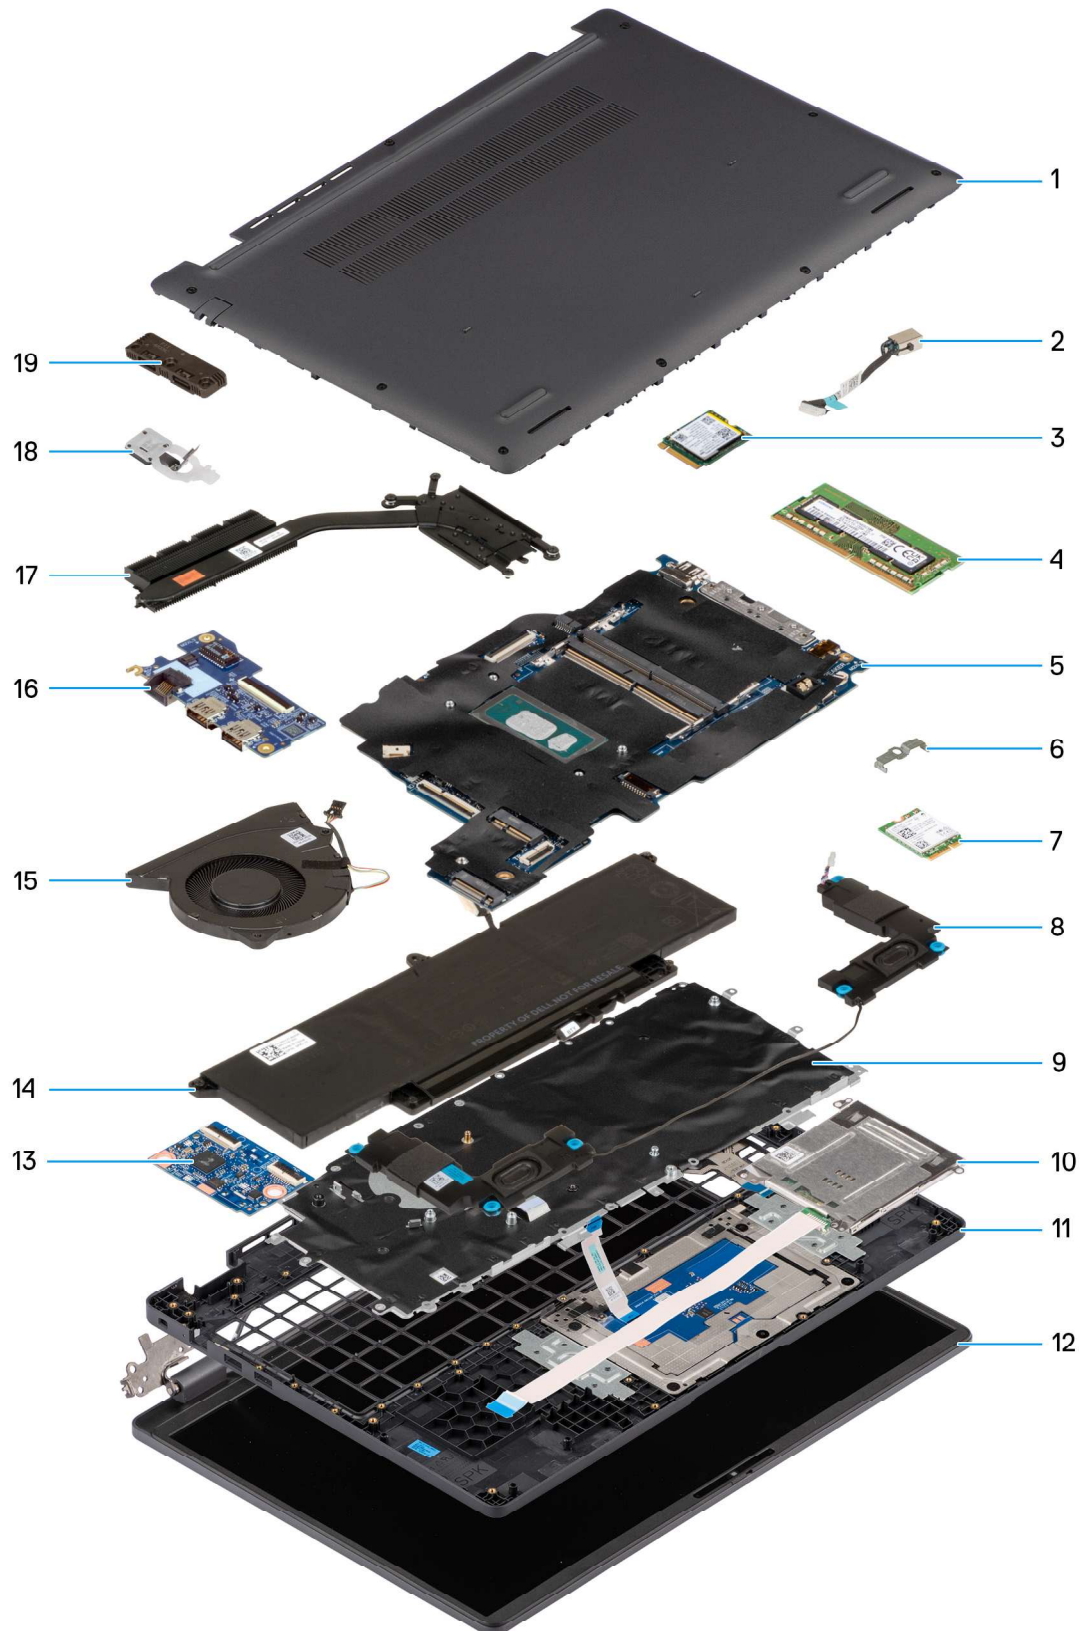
Hauptkomponenten des Systems/Explosionsansicht
